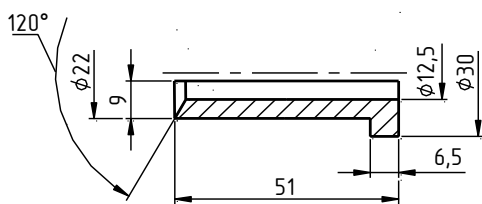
Чертеж детали, получаемой *разрезкой заготовки* на части и являющейся *взаимозаменяемой* на другие детали, получаемые из других заготовок
